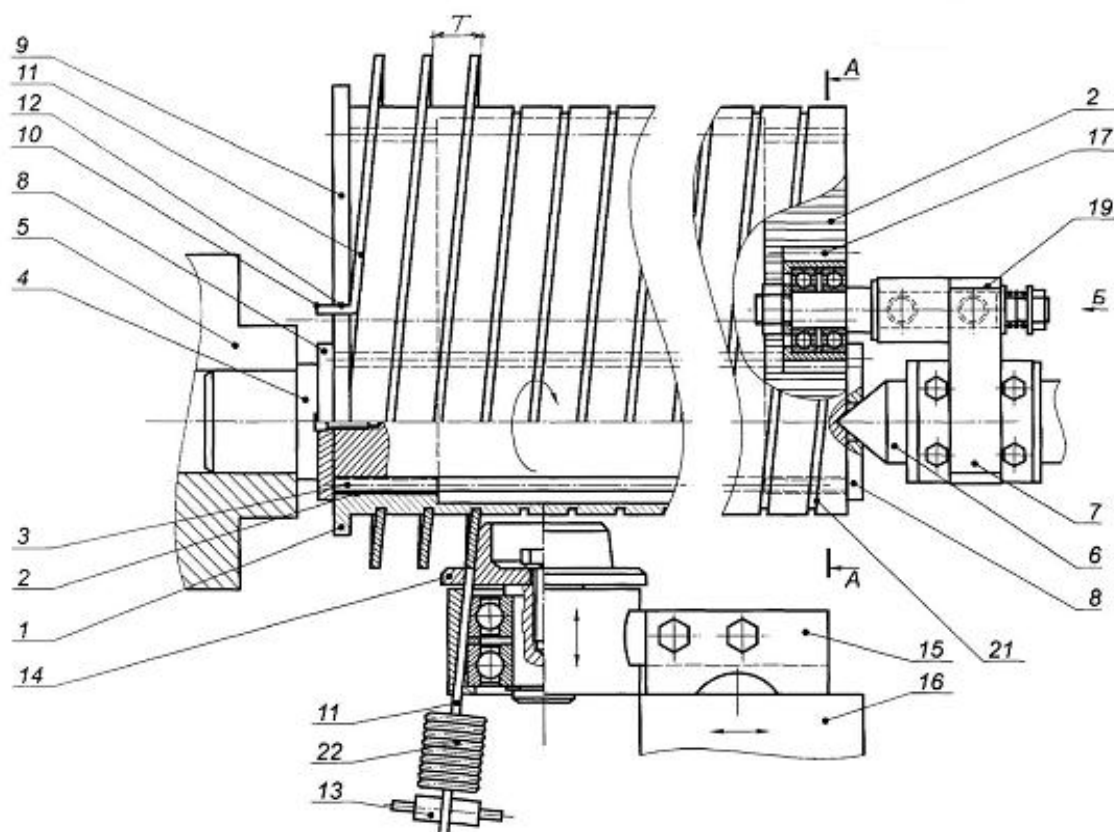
Пристрій для виготовлення гвинтових еліпсних заготовок
